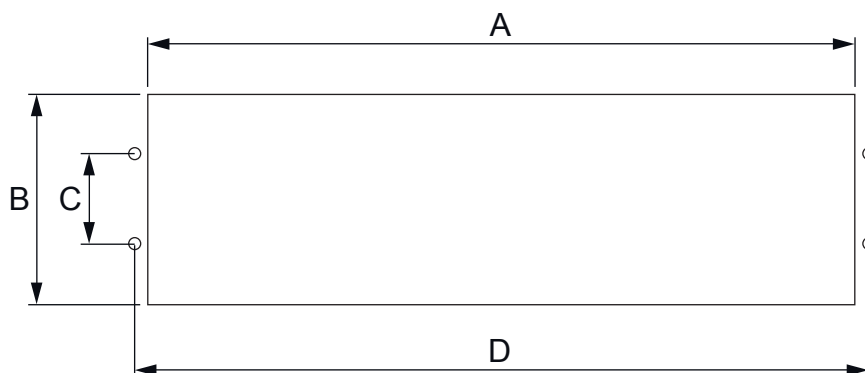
Dimensiones existentes de marco de panel para SPAC 510, SPAC 520 y SPAC 530
